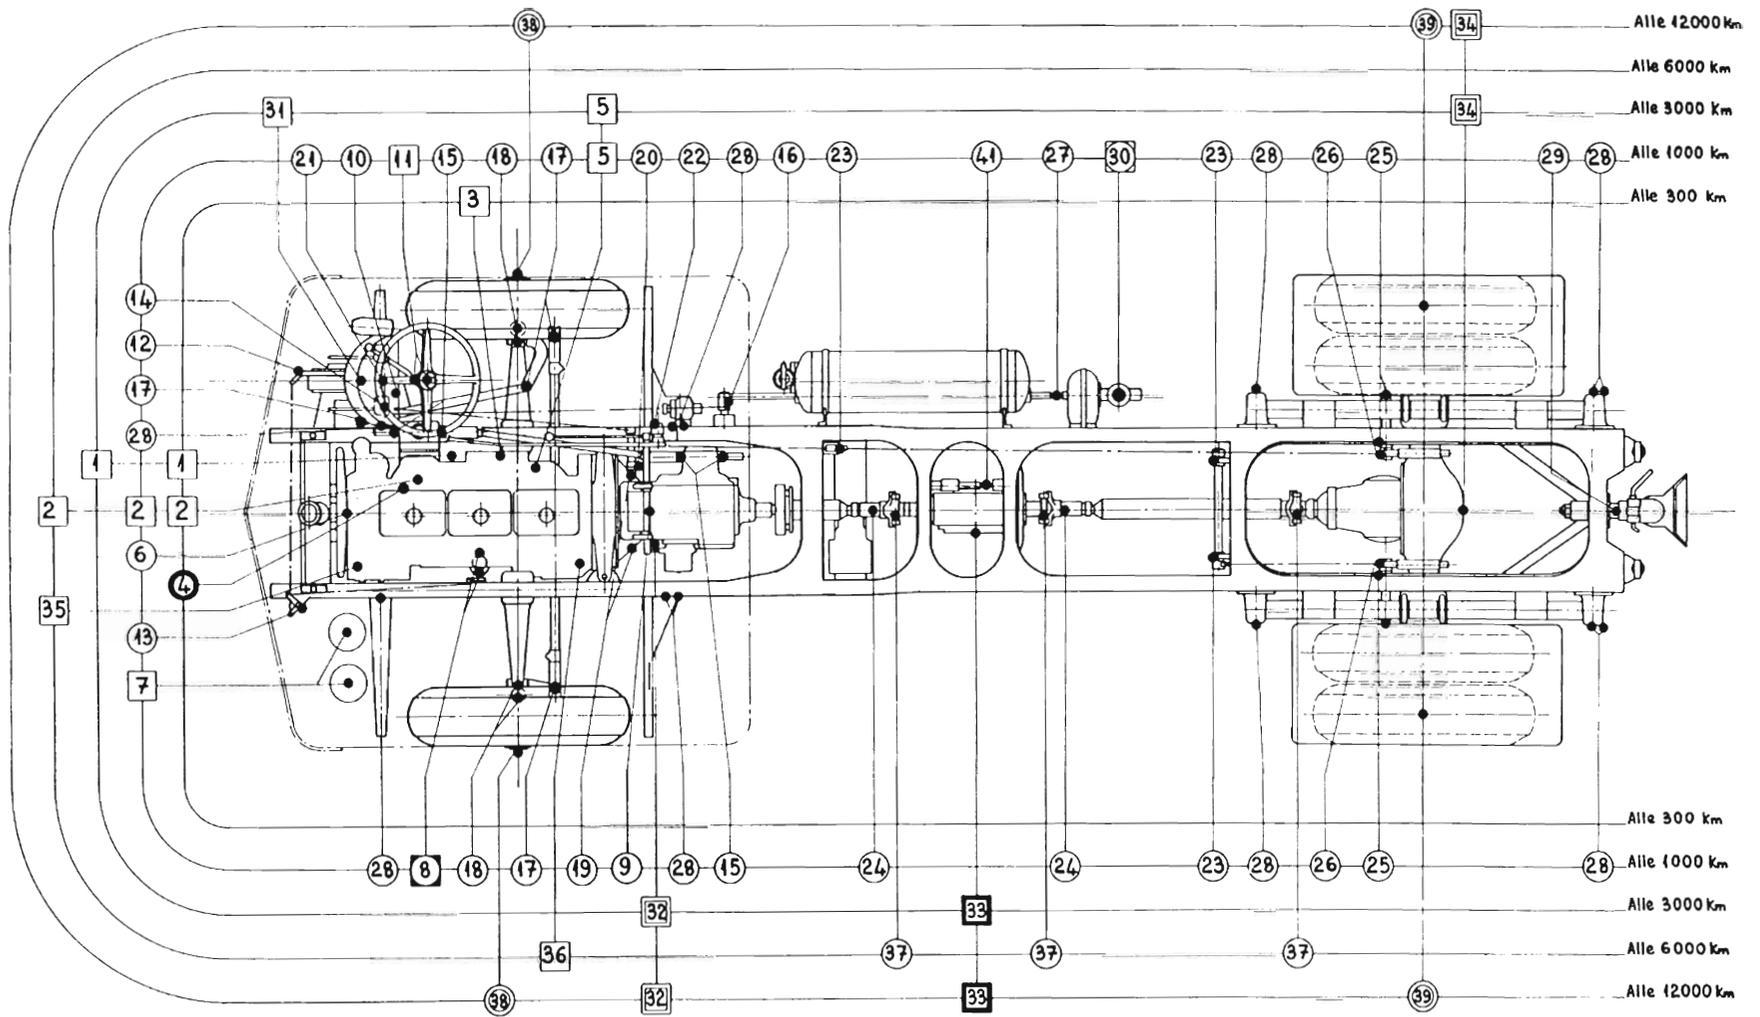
Schmierplan zu DD-Motor und Chassis Type AS 45-V (Frontlenker)
